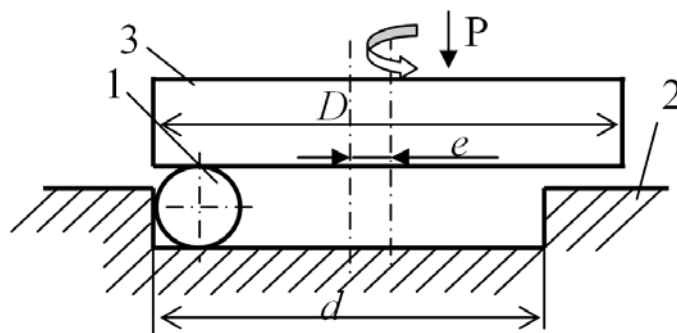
Схема накатывания сферической заготовки плоскими поверхностями
